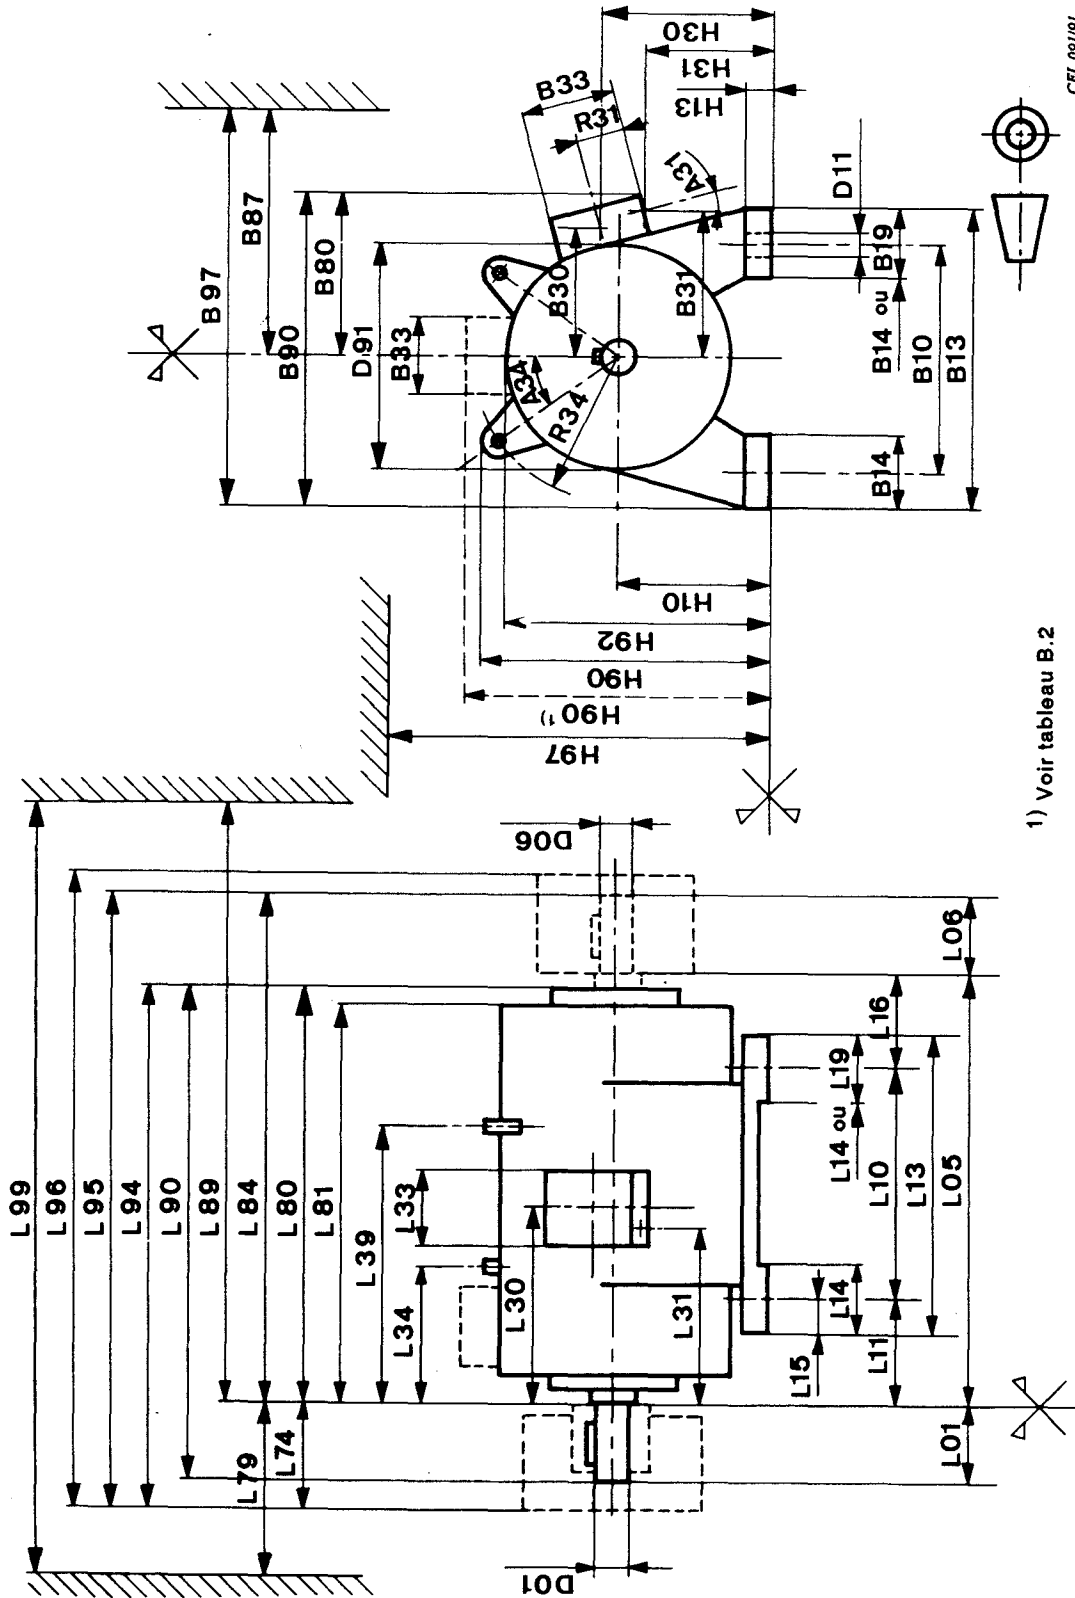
Dimensions de montage pour machines à fixation par pattes
